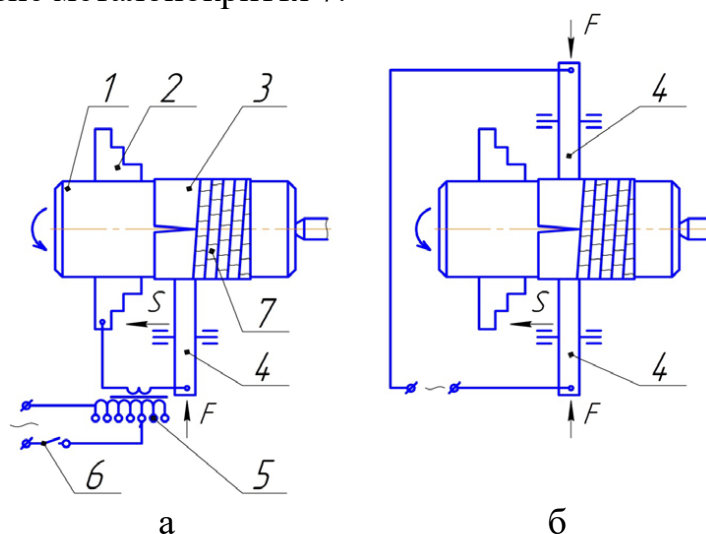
Технологічні схеми відновлення валів електроконтактним приварюванням сталевих стрічок: а – однороликова схема наплавлювання; б – двороликова схема; 1 – відновлювана деталь; 2 – патрон 3 – присадочна стрічка; 4 – ролик-електрод; 5 – зварювальний трансформатор; 6 – переривач струму; 7 – металопокриття
